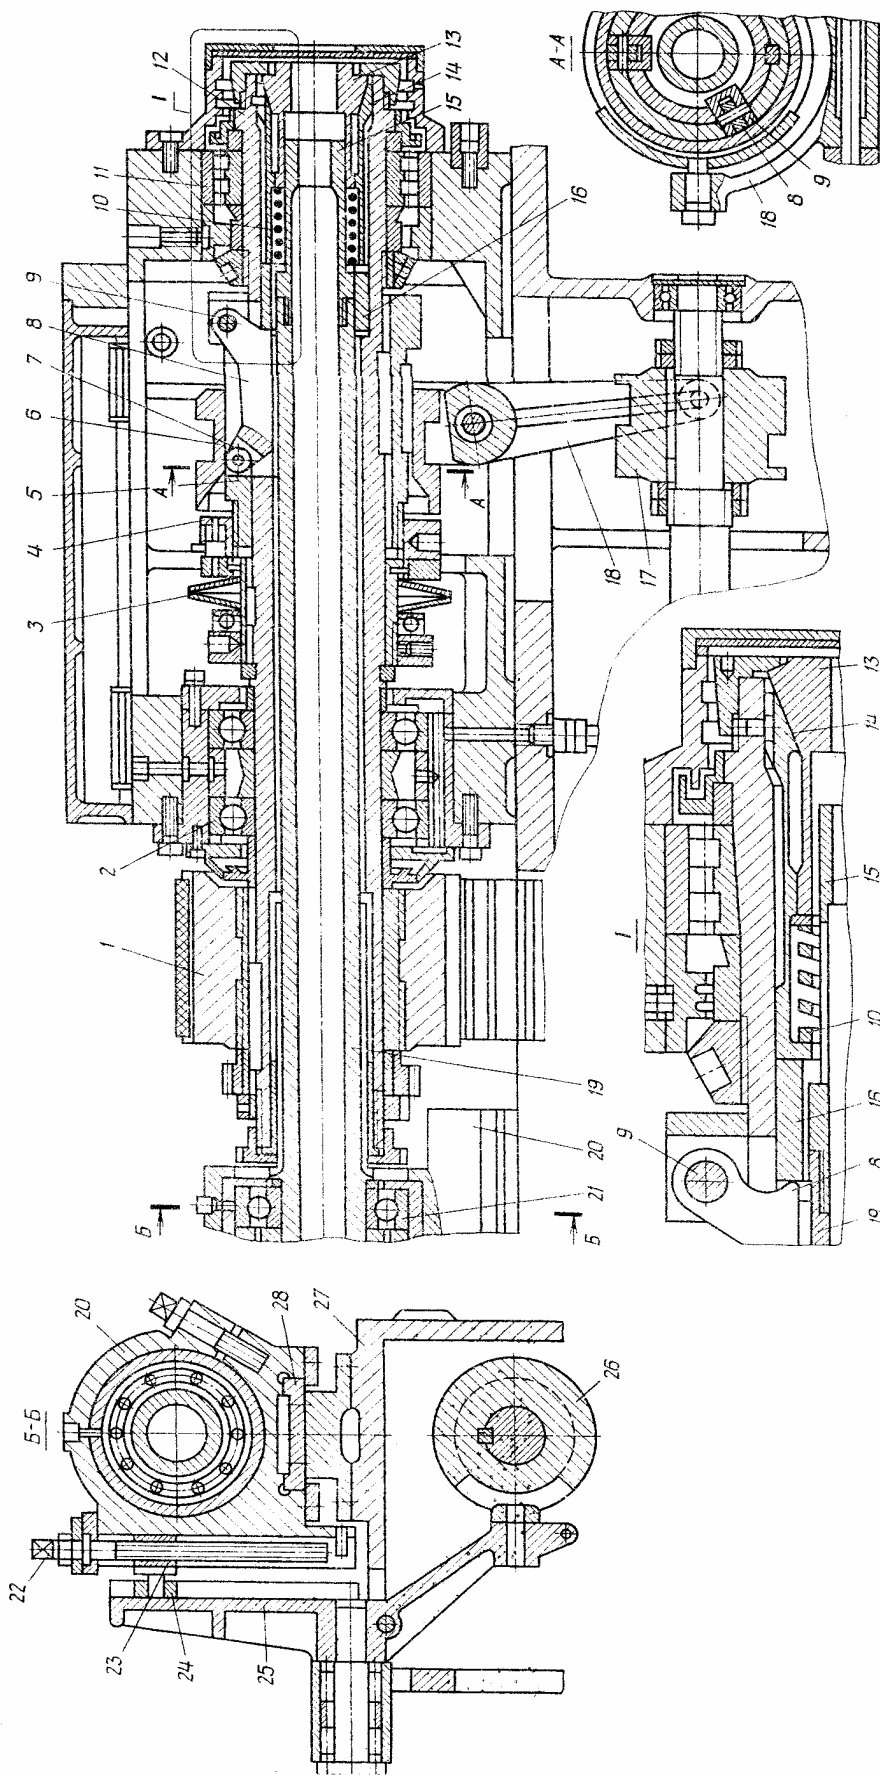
Шпиндельна бабка токарно-револьверного автомата мод. 1E140П
